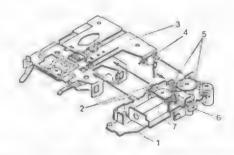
1 — шасси привода механизма микролифта; 2 — направляющие пазы; 3 — кассетоприемник; 4 — пружина привода кассетоприемника; 5 — основные швстерни привода микролифта; 6 — чераячная шестерня; 7 — электродвигатель привода механизма микролифта
